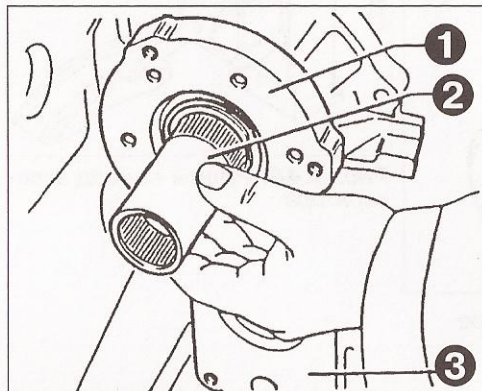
Установка трубчатого вала в картер распределительного механизма.
